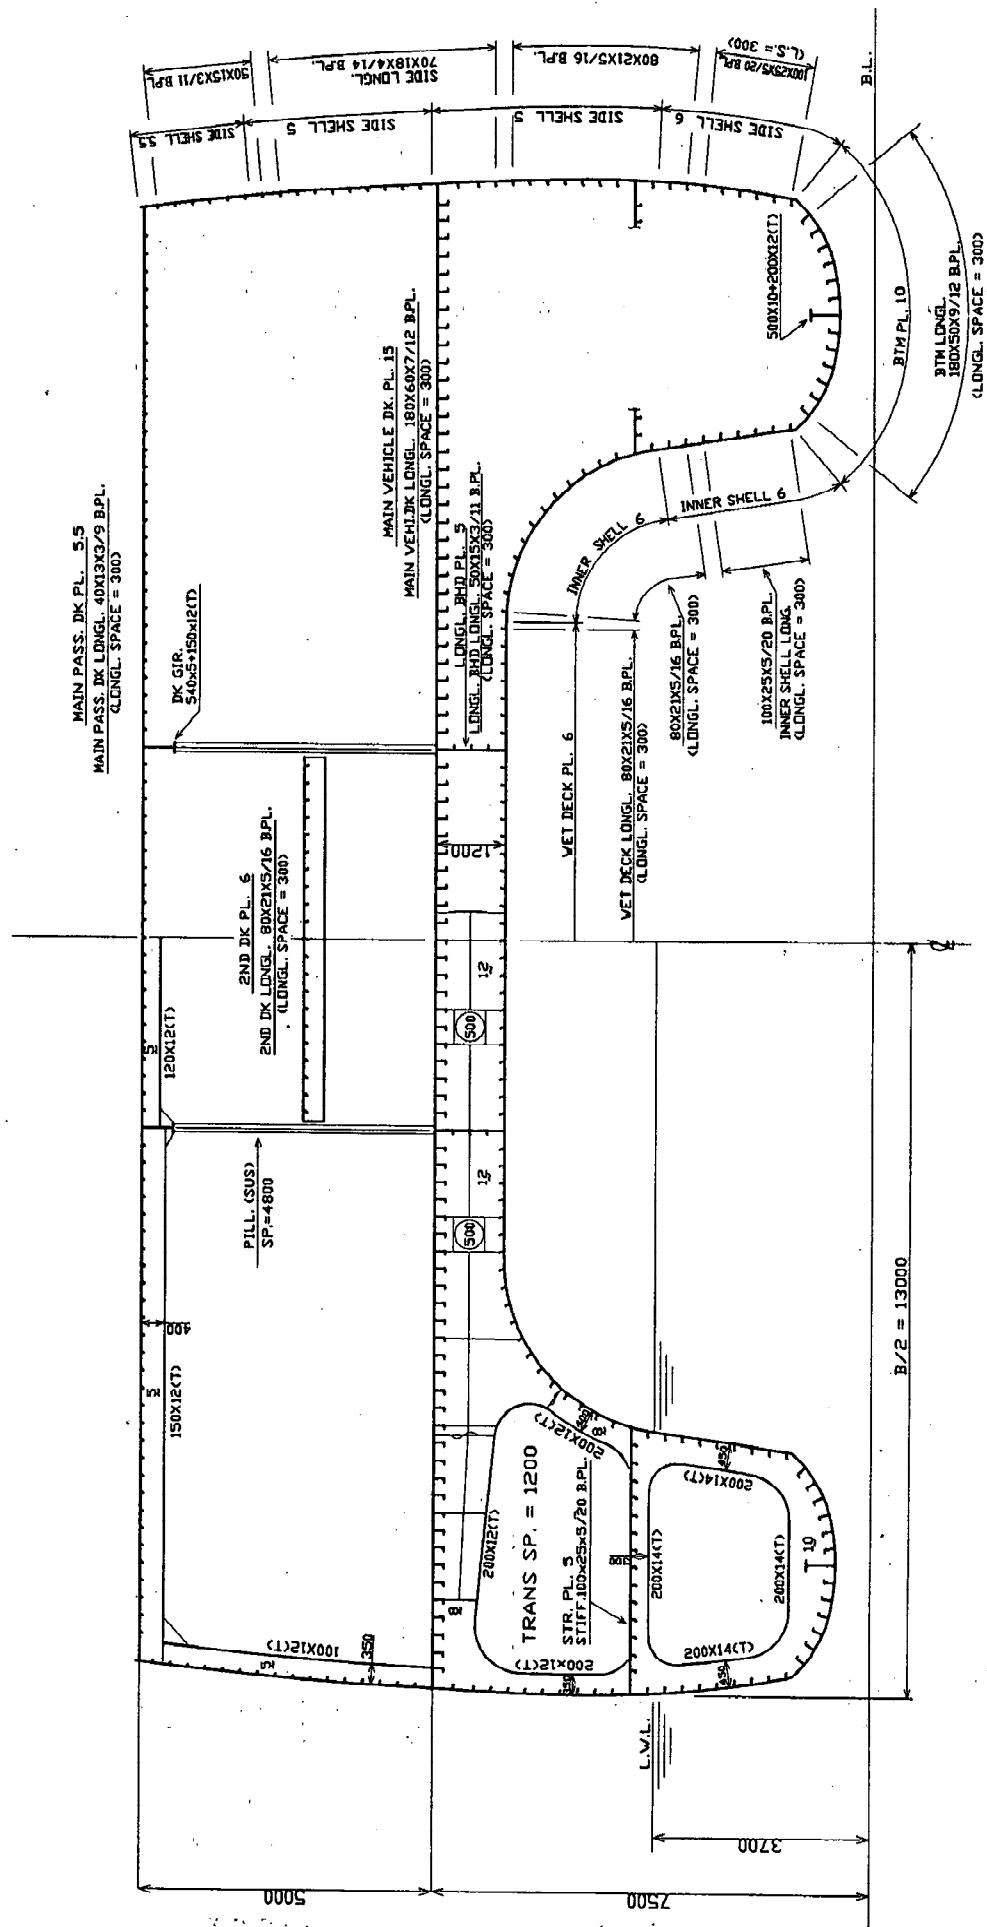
双胴船 INCAT 96m型中央横断面図
